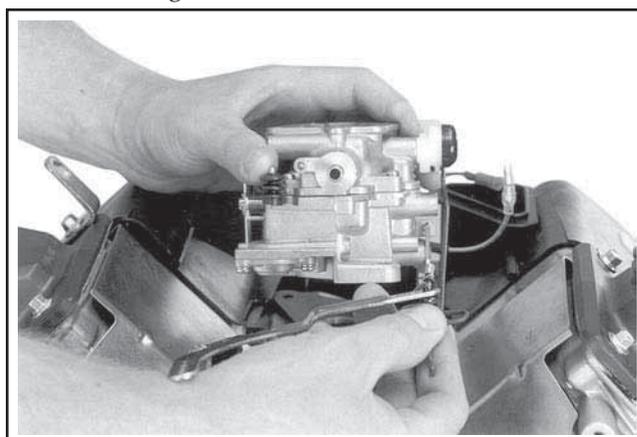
Enlèvement du groupe carburateur avec le levier du régulateur.
